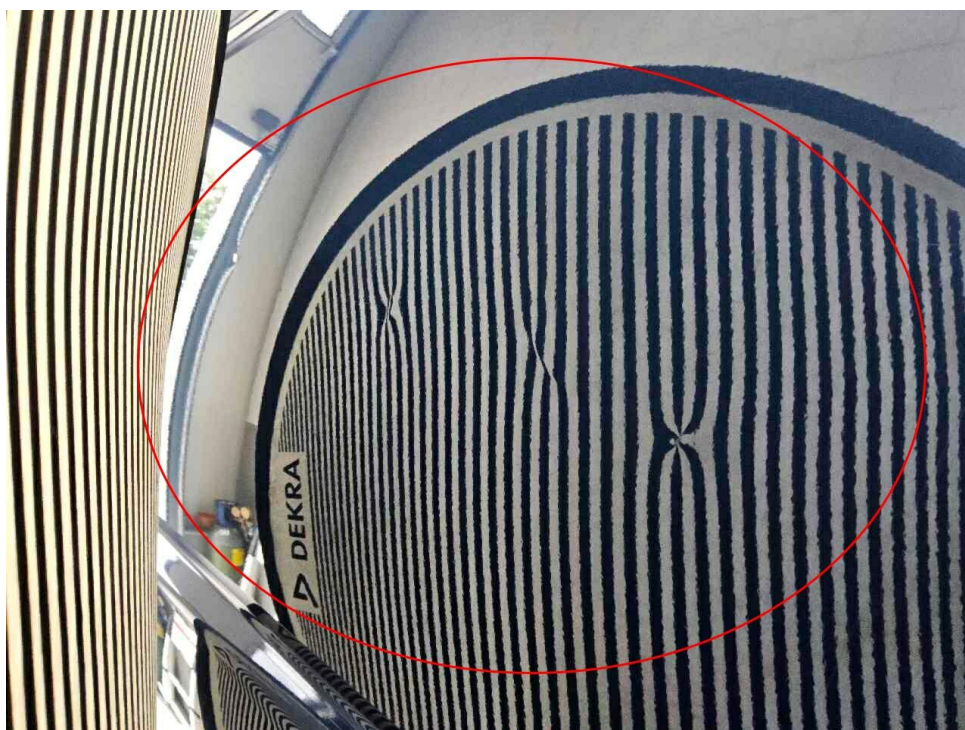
Schiebetür rechts, mehrfach eingedellt, instandsetzen und lackieren mit Lackaufbau
